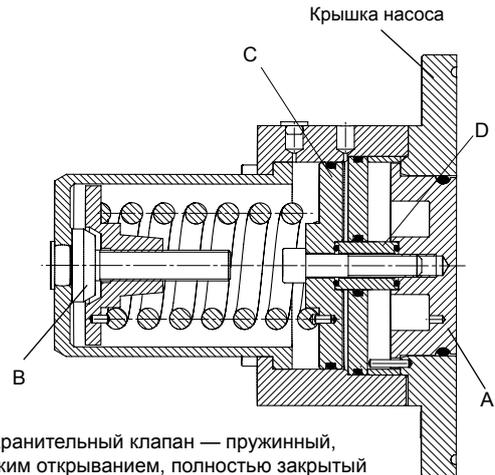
Предохранительный клапан — пружинный, с пневматическим открыванием, полностью закрытый
